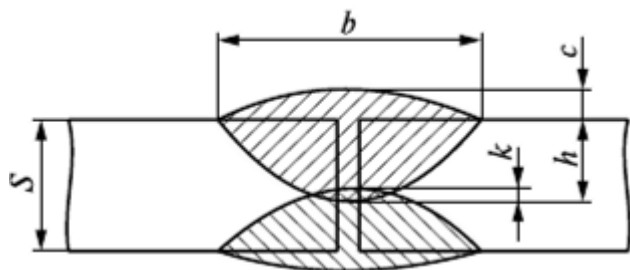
Схема двустороннего стыкового сварного соединения
